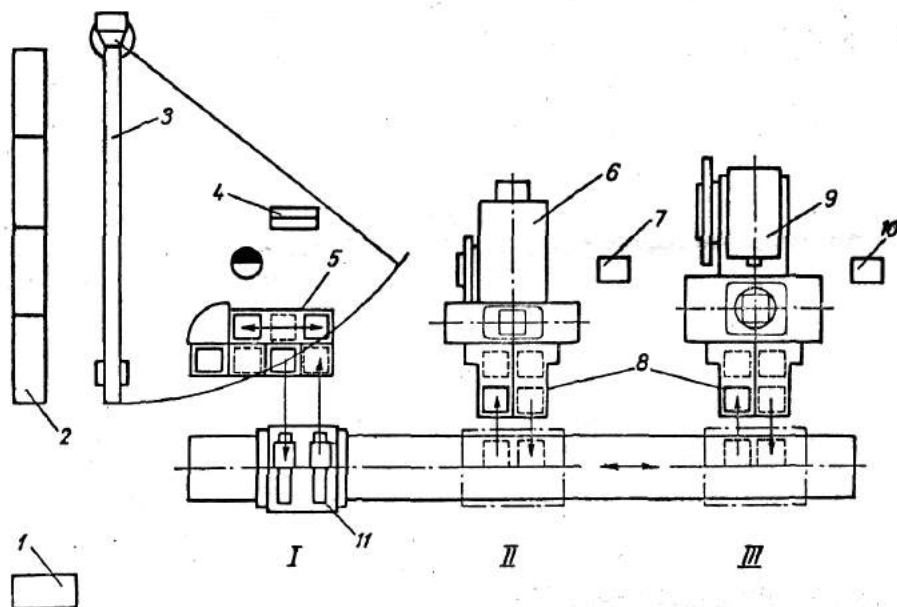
Гнучка виробнича система для обробки корпусів:
